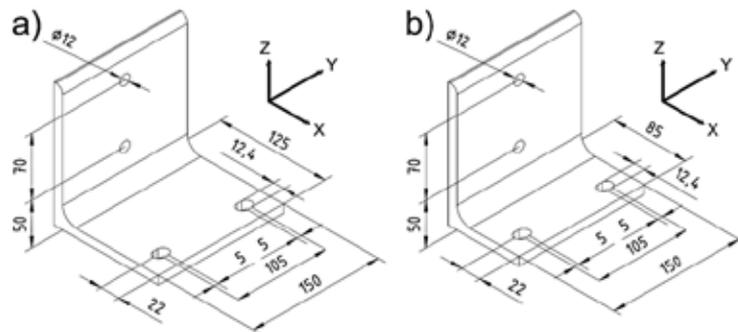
Supports muraux – version: a) version standard, b) version raccourcie
